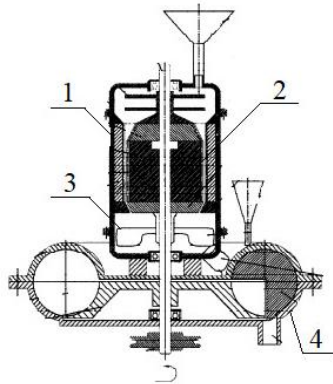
РЦА с торообразным смесителем: 1- камера измельчения; 2- ротор; 3- лопастной питатель; 4- торообразный смеситель.
